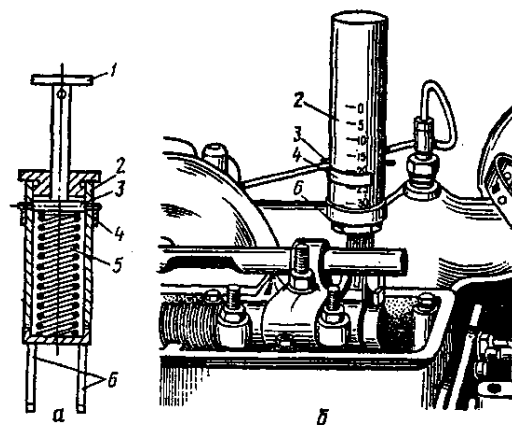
Перевірка пружності пружини клапанів газорозподілу приладом КИ-723: а - прилад для перевірки зусилля притискування клапанів до сідел головки циліндрів; б - визначення зусилля притискування клапану до сідла; 1 - рукоятка приладу; 2 - корпус; 3 - натискний штифт; 4 - кільцефіксатор; 5 - пружина; 6 - встановлювальні стійки.
